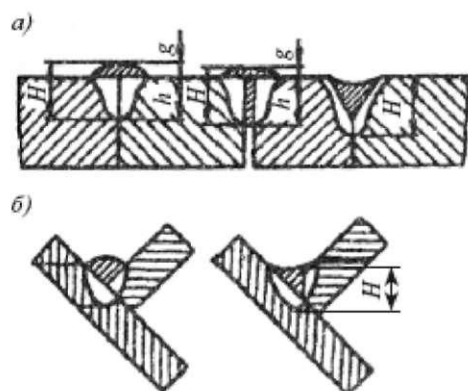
Влияние зазора и разделки на форму шва: а - при стыковых швах; б - при угловых швах; Н - общая высота шва; h - глубина провара; g - высота выпуклости шва
